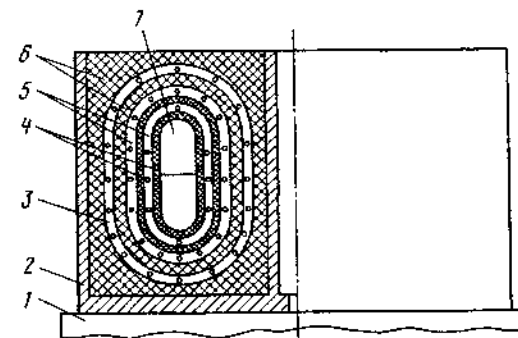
Конструкция высоковольтного трансформатора в металлическом корпусе
